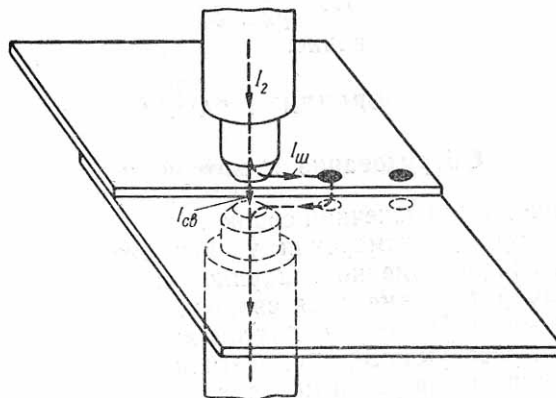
Шунтирование тока при точечной сварке
